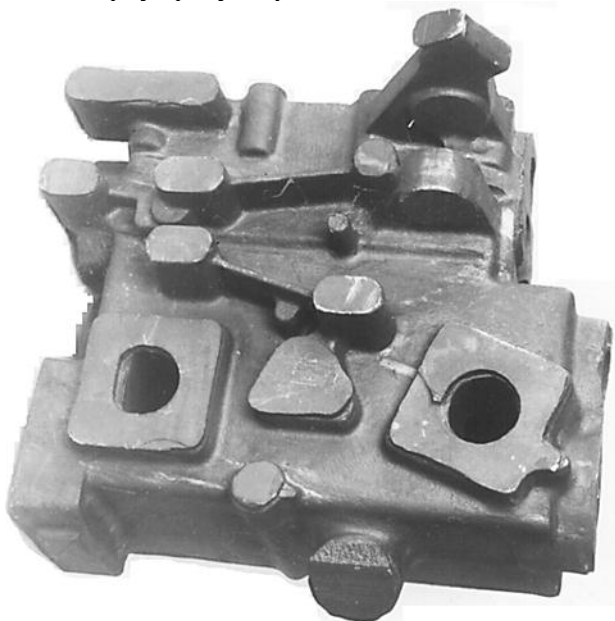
Корпус редуктора из магниевого сплава МЛ8
